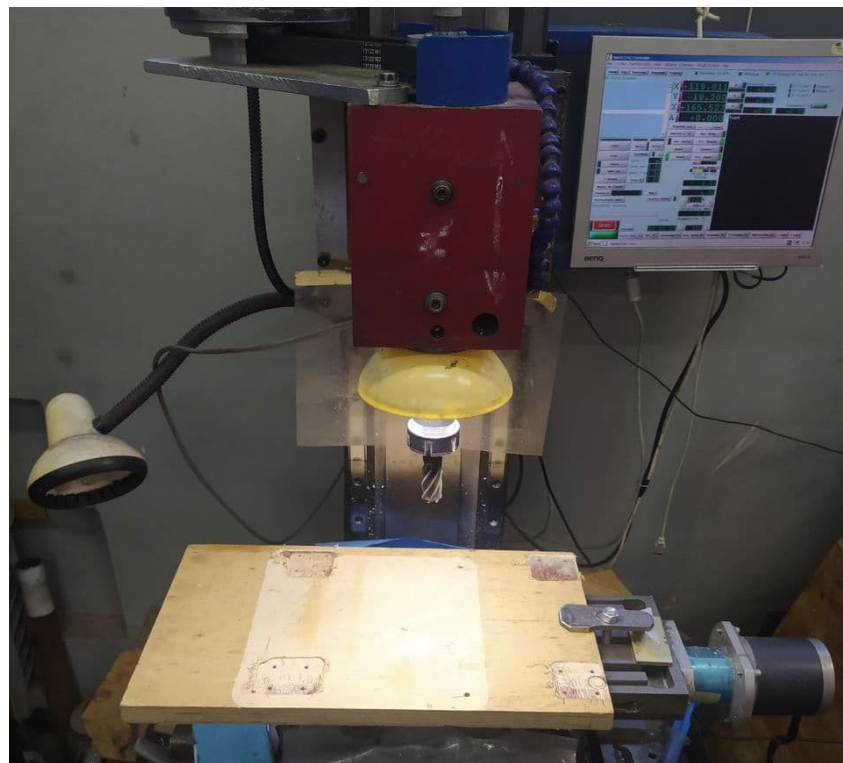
Фрезерувальний верстат з ЧПК профрезерував та просвердлив отвори каретки
